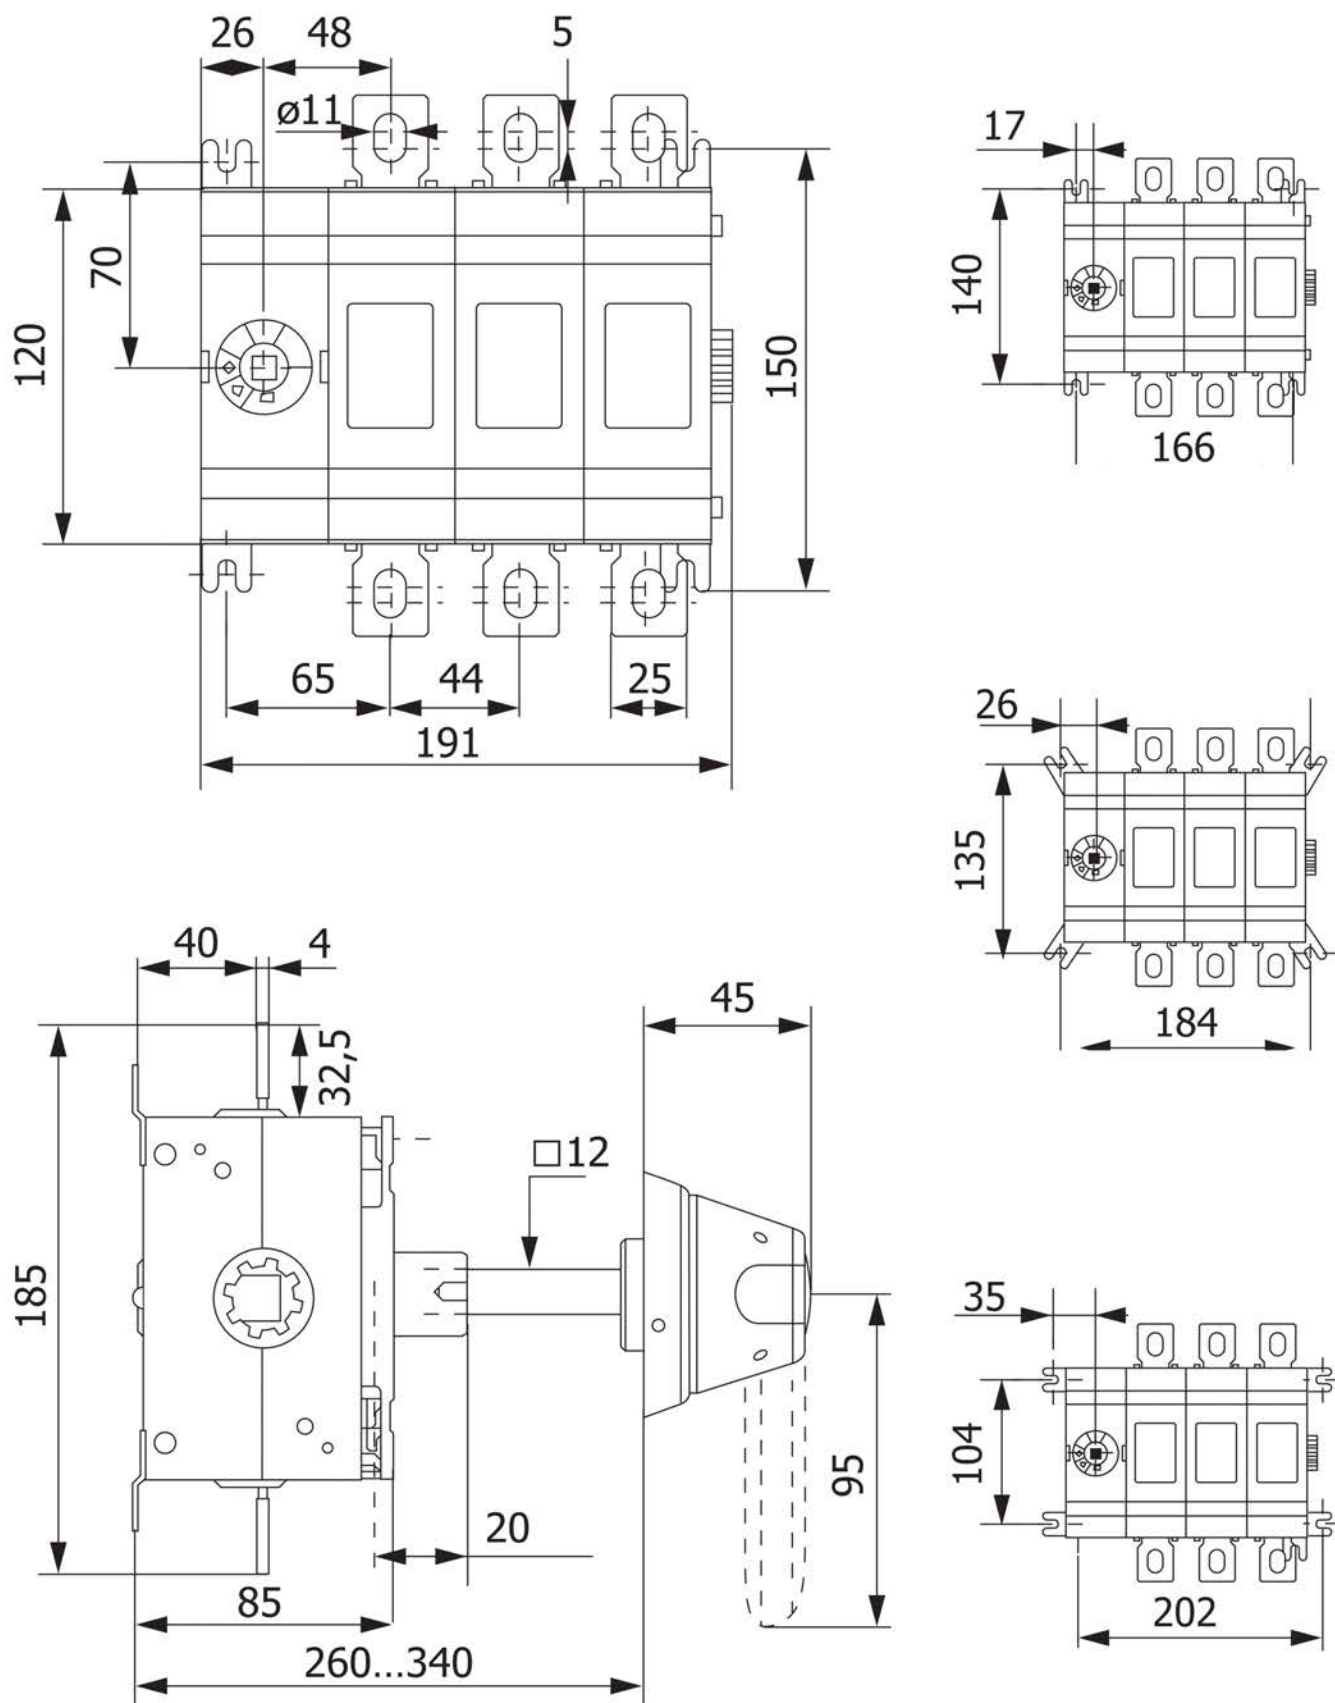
Габаритные и установочные размеры рубильников 315-400 А
